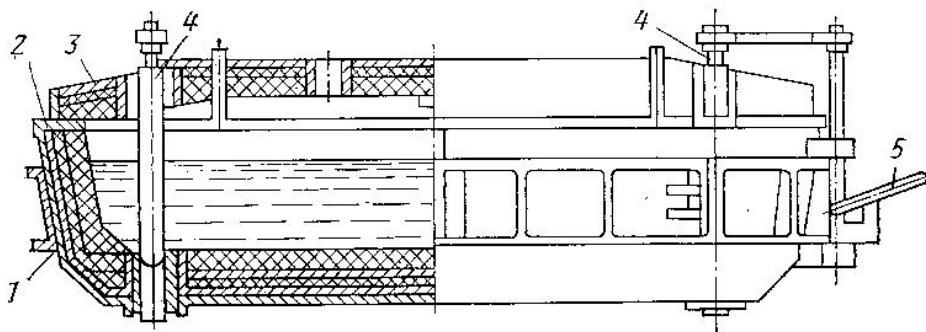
Промежуточный ковш: 1 — ребра жесткости; 2 — сварной корпус; 3 — крышка; 4 — стопорный механизм; 5 — ручка управления стопорным механизмом
